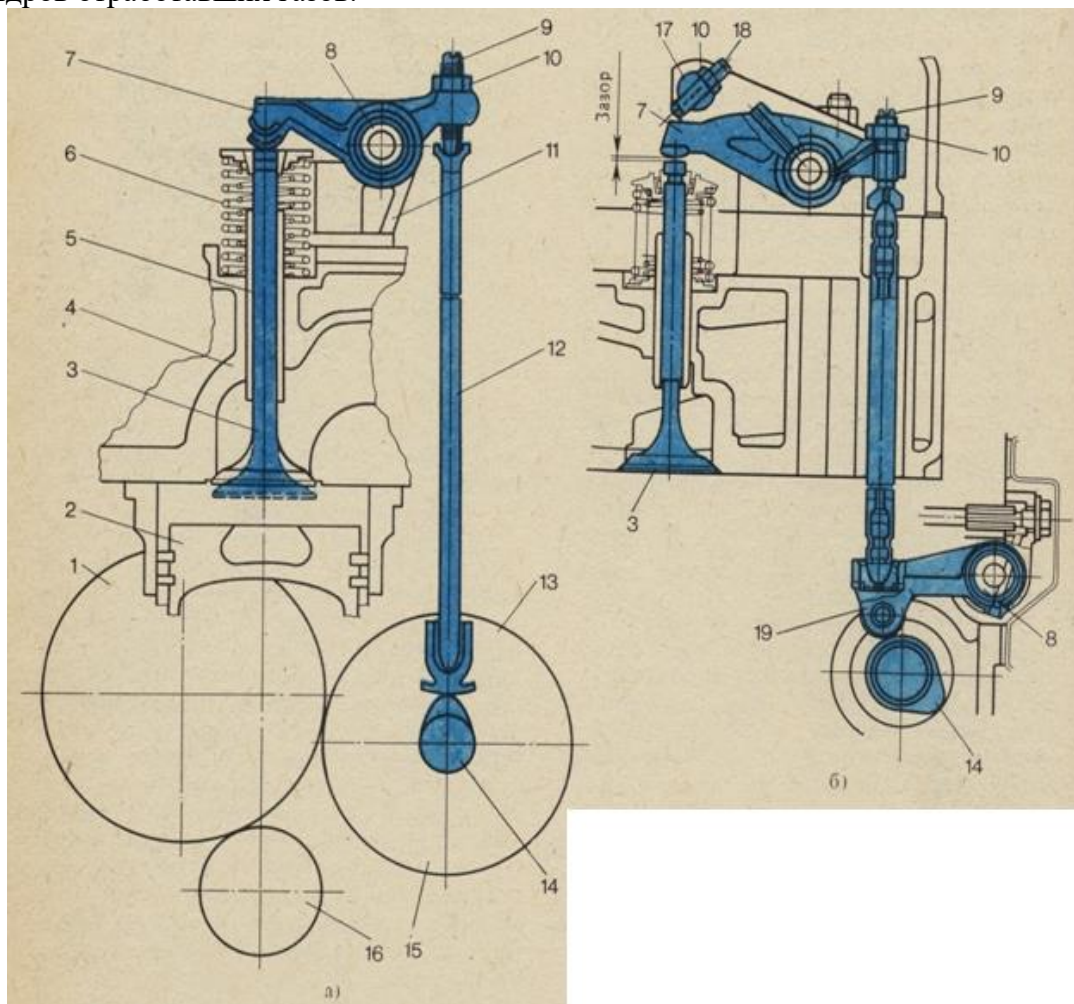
Схемы газораспределительных механизмов: а - с грибовидным толкателем, б - с качающимся толкателем; 1 - промежуточная шестерня, 2 - поршень, 3 - клапан, 4 - головка цилиндров, 5 - направляющая втулка, 6 - пружины клапана, 7 - коромысло, 8 - ось (валик) коромысла, 9 - регулировочный винт, 10 - контргайка, 11 - стойка валика коромысла, 12 - штанга, 13 - толкатель, 14 - распределительный вал, 15 - шестерня распределительного вала, 16 - шестерня коленчатого вала, 17 - валик декомпрессора, 18 - регулировочный винт декомпрессора, 19 - качающийся толкатель.
